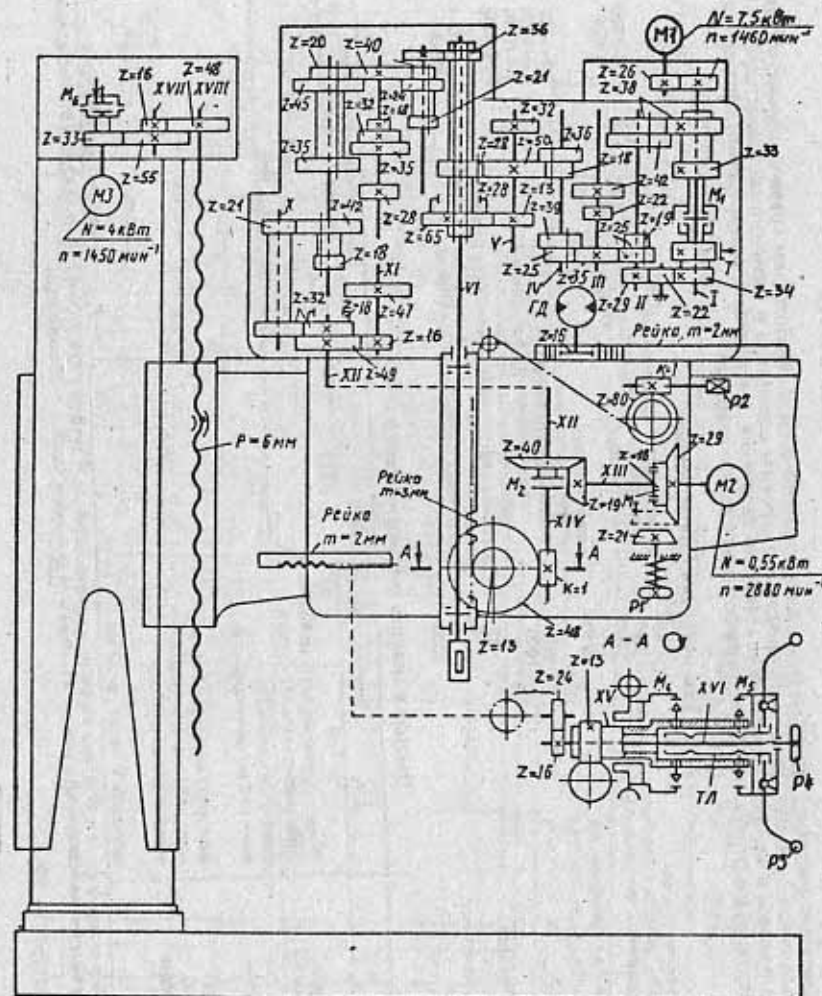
Кинематическая схема радиально-сверлильного станка
